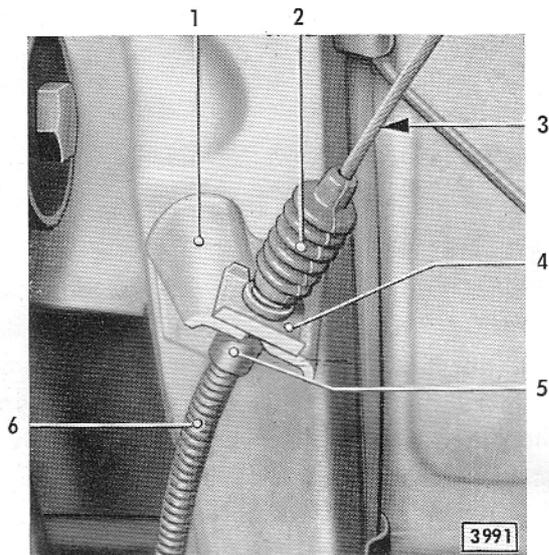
Druckschlauch für hinteres Handbremsseil am Wagenboden befestigt
